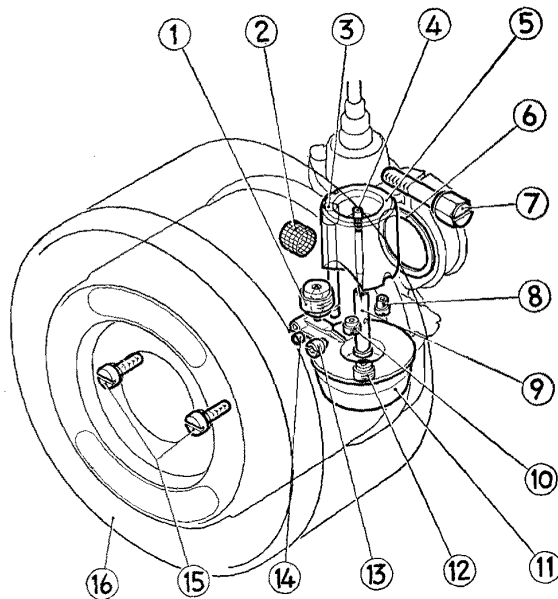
Carburador ZENITH: Limpieza e inspección.
